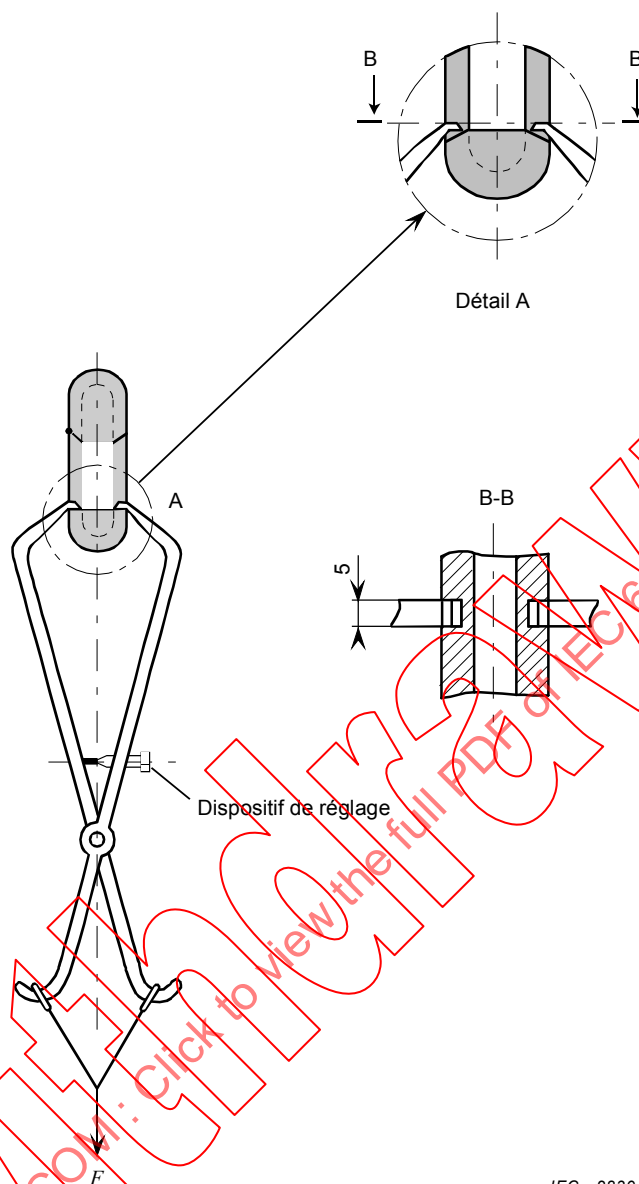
Principe du dispositif d'essai pour vérifier l'adhérence du revêtement isolant sur les parties conductrices des outils (voir 5.7.2)
